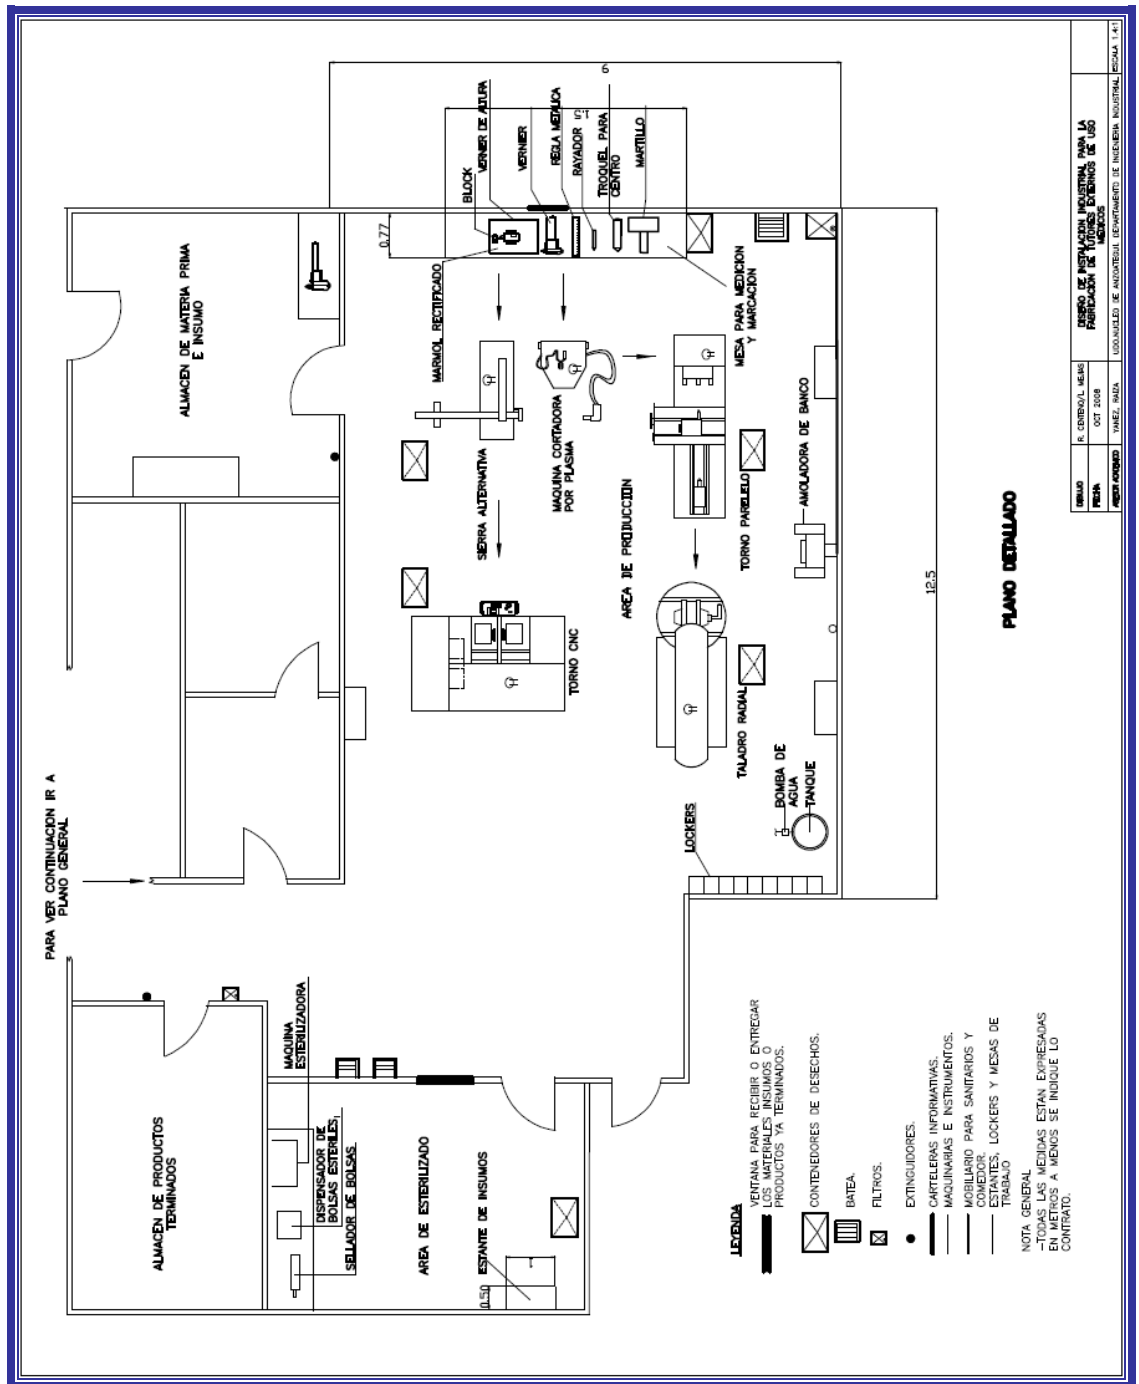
Plano de distribución de los equipos en el área de producción de la planta
